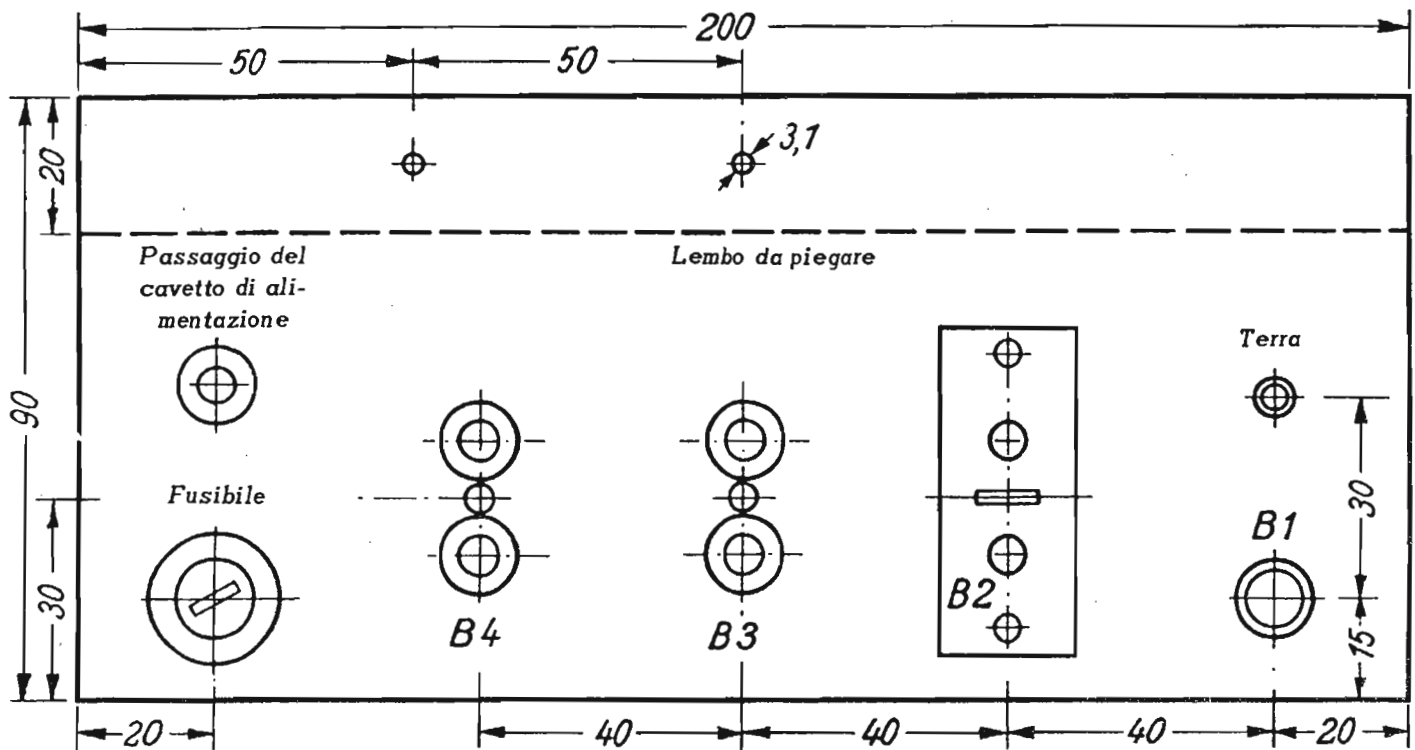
Disposizione delle singole parti sulla striscia dei collegamenti.
